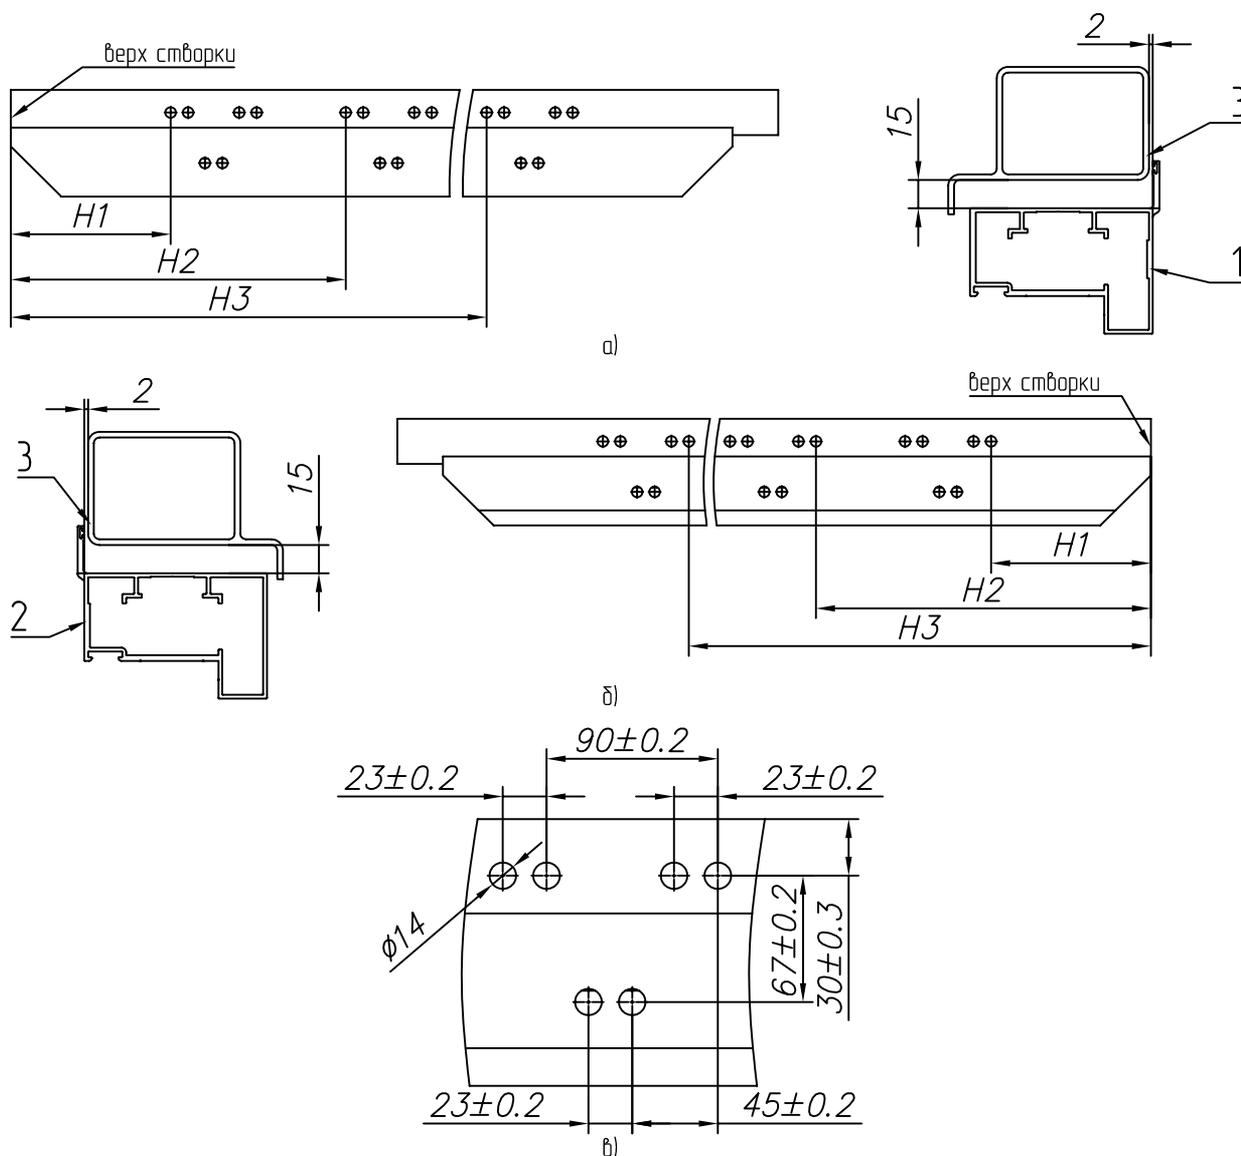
Изготовление групп отверстий для крепления петель:
